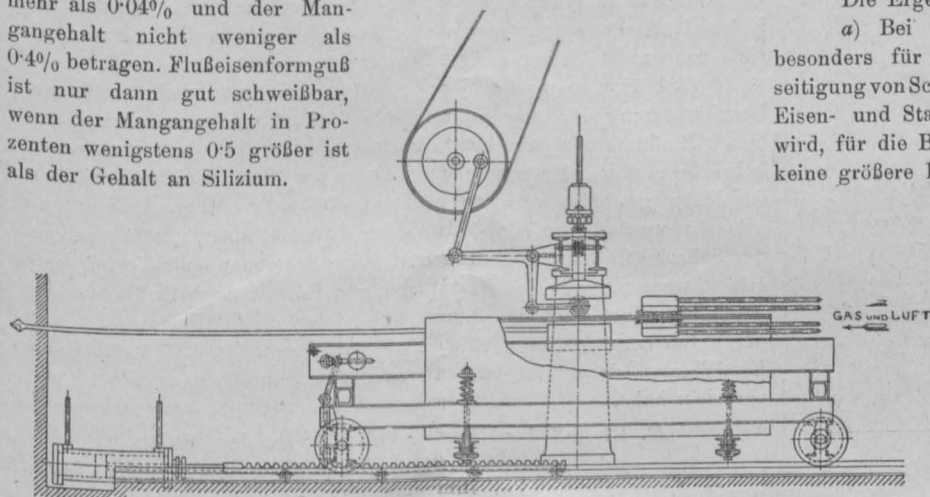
Apparat für hydraulische Maschinenschweißung mittels Rolle
